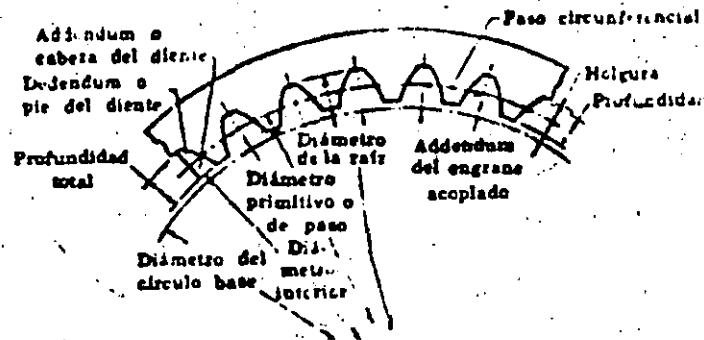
TERMINOLOGIA DE UN ENGRANAJE INTERNO
